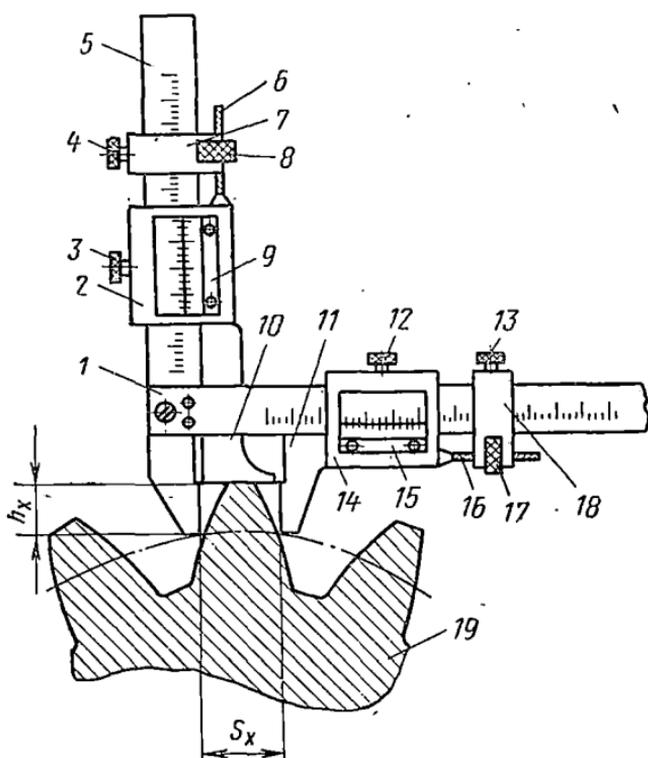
Измерение толщины зуба шестерни штангензубомером:
